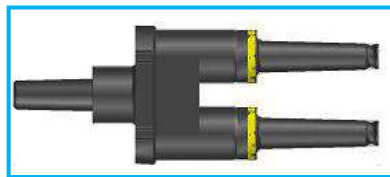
BOQUILLA TIPO INSERTO DOBLE [6]
